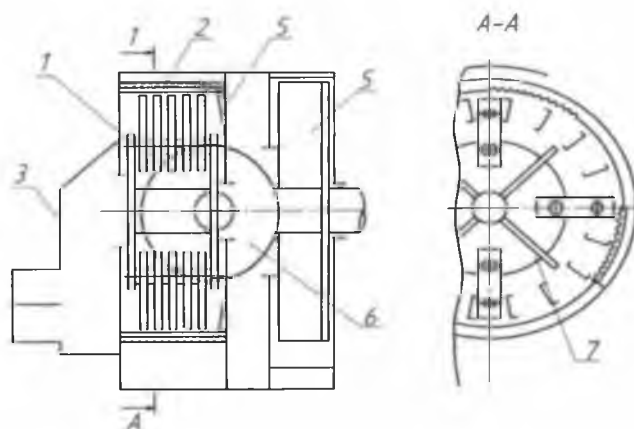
Схема зернодробарки: 1 – молотковий ротор; 2 – дека; 3 – сепаратор; 4 – колесо вентилятора; 5 – жалюзійне решето; 6 – вхідний отвір корпуса вентилятора; 7 – лопатка ротора.
